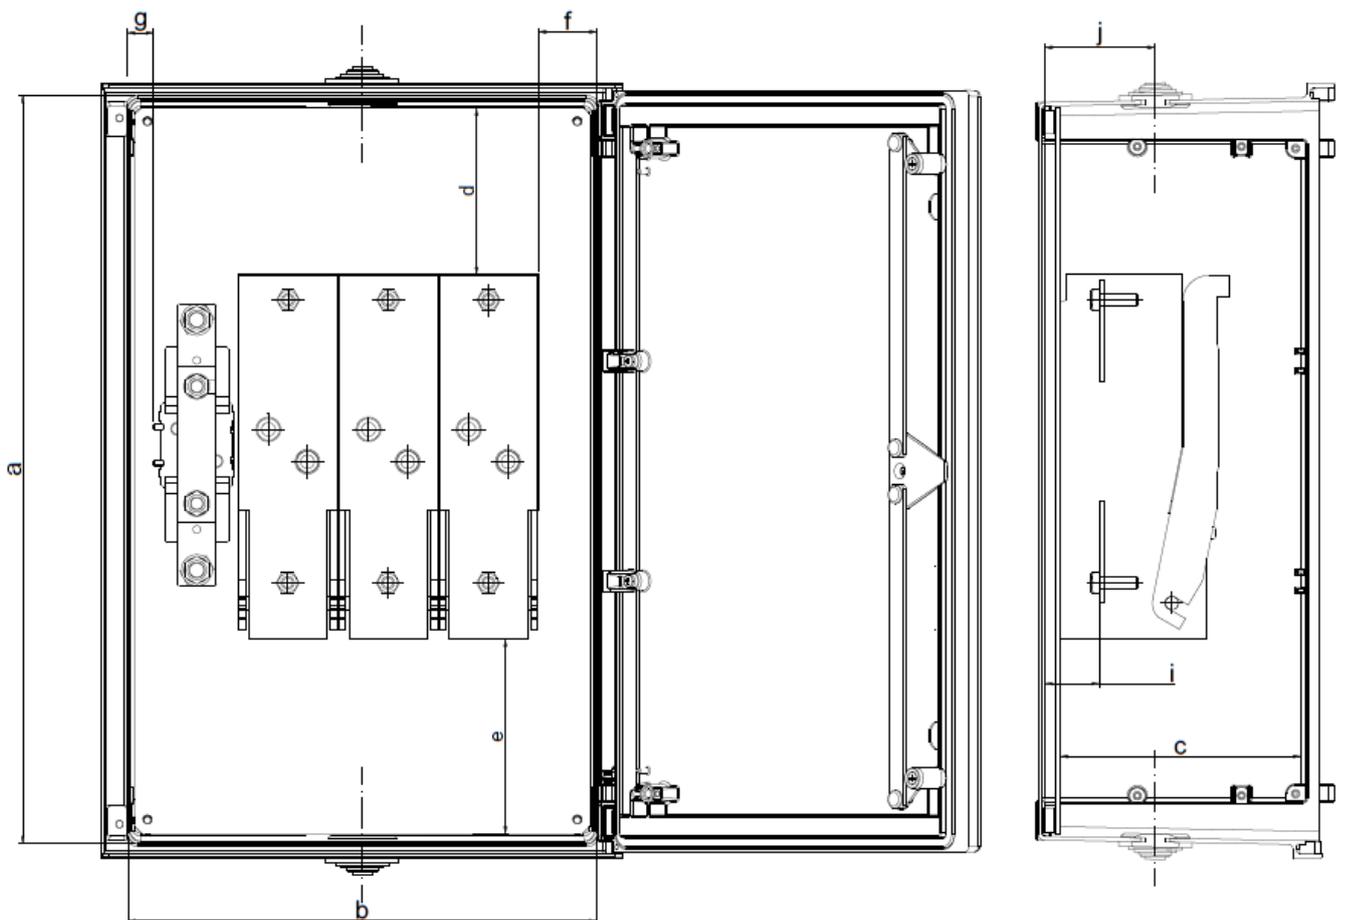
Portinhola PBTE 400 – Disposição e dimensões
